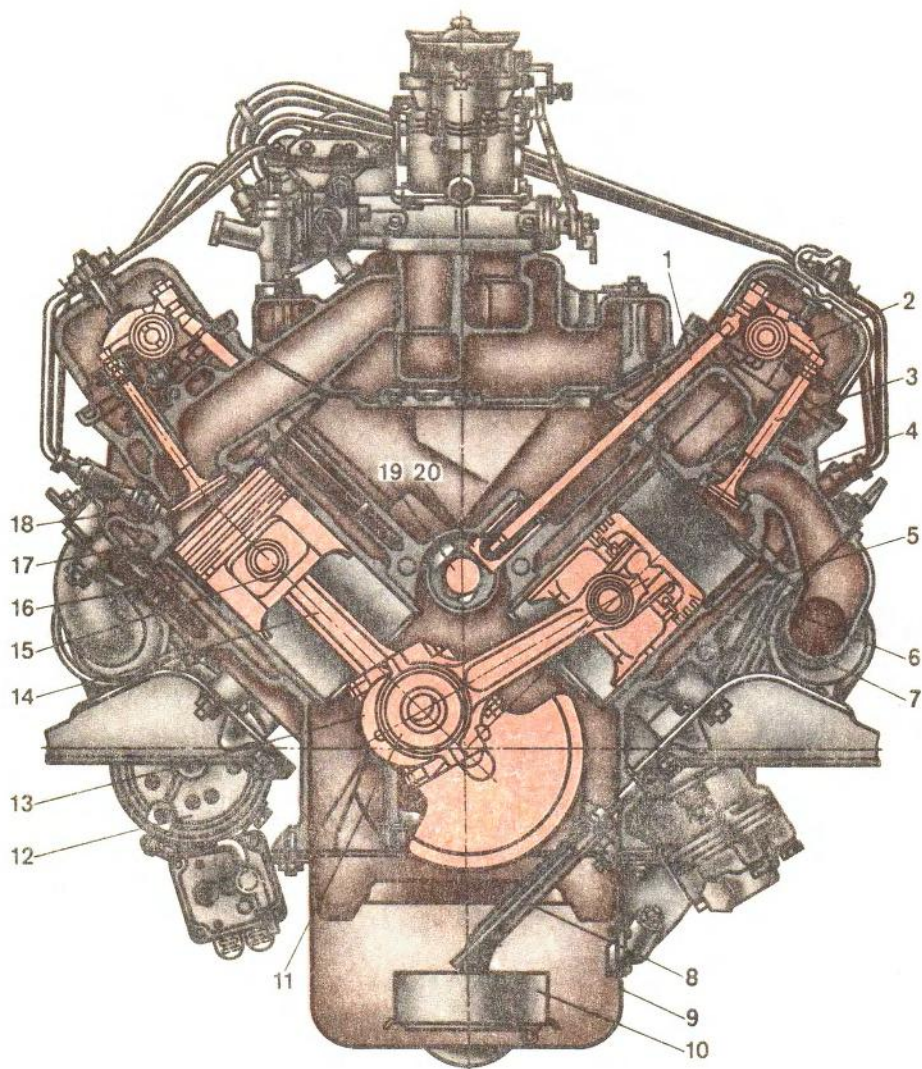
Поперечный разрез двигателя ЗМЗ-53-11:
